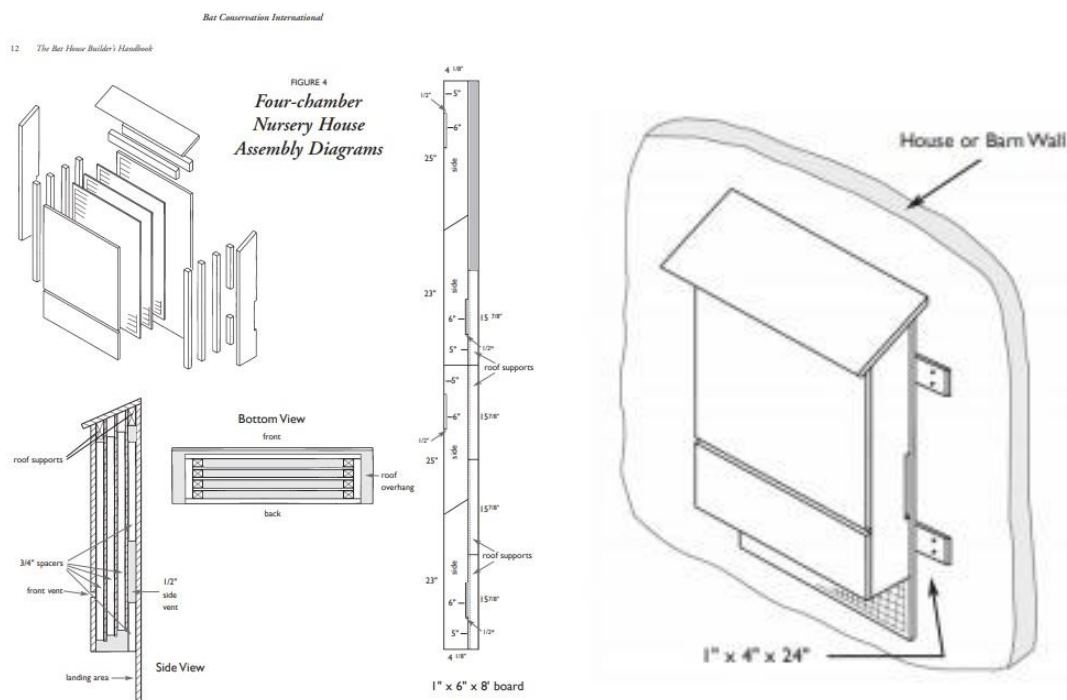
Caseta plana para murciélagos. a) dimensiones y manera de construirla; (b) caseta armada donde se señala el tipo de anclaje a un muro o árbol.
